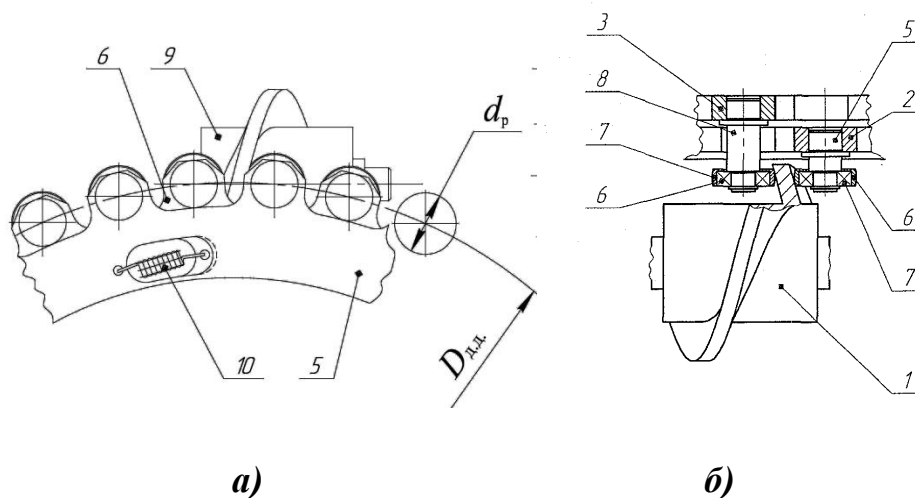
Червячно-роликовая передача: а) вид сбоку:
